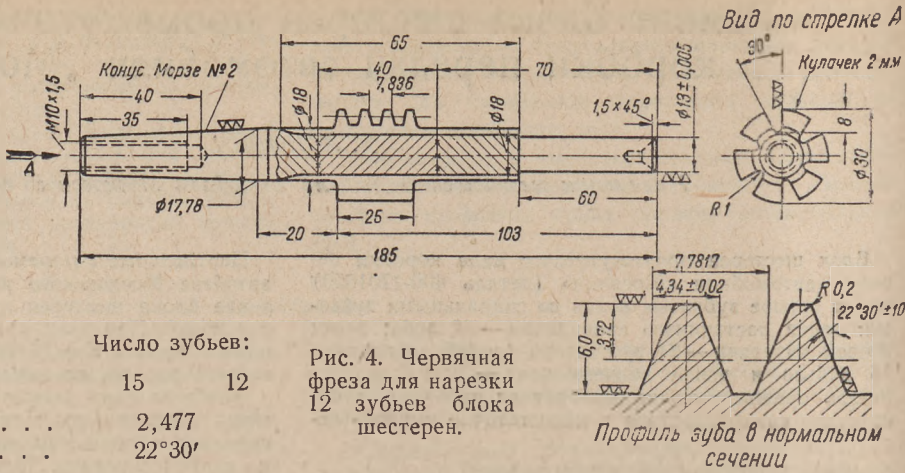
Червячная фреза для нарезки 12 зубьев блока шестерен.
